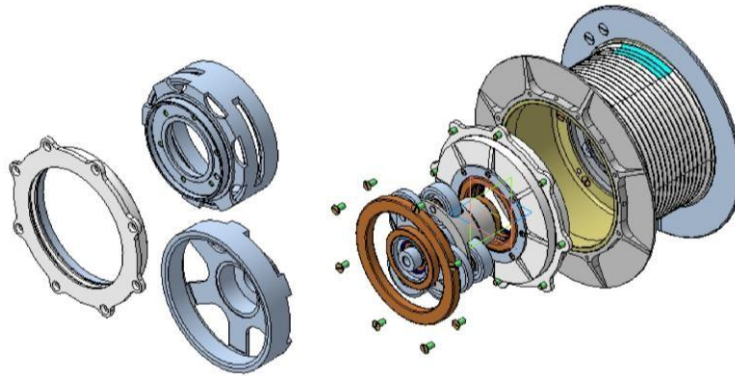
Сборочная единица и детали, обрабатываемые на токарно-фрезерных центрах
